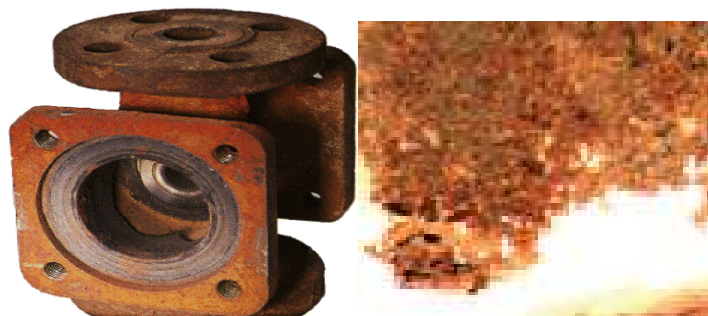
Corrosion généralisée ou uniforme des pièces en acier.
